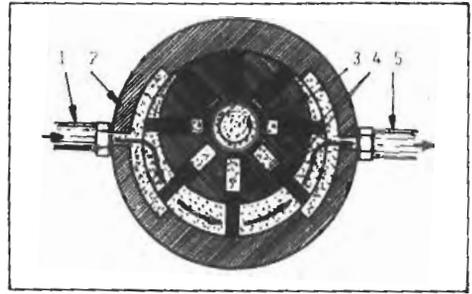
Motor hidráulico de paletas. 1.- Entrada del aceite a presión. 2.- Cilindro. 3.- Rotor. 4.- Paletas. 5.- Retorno.
